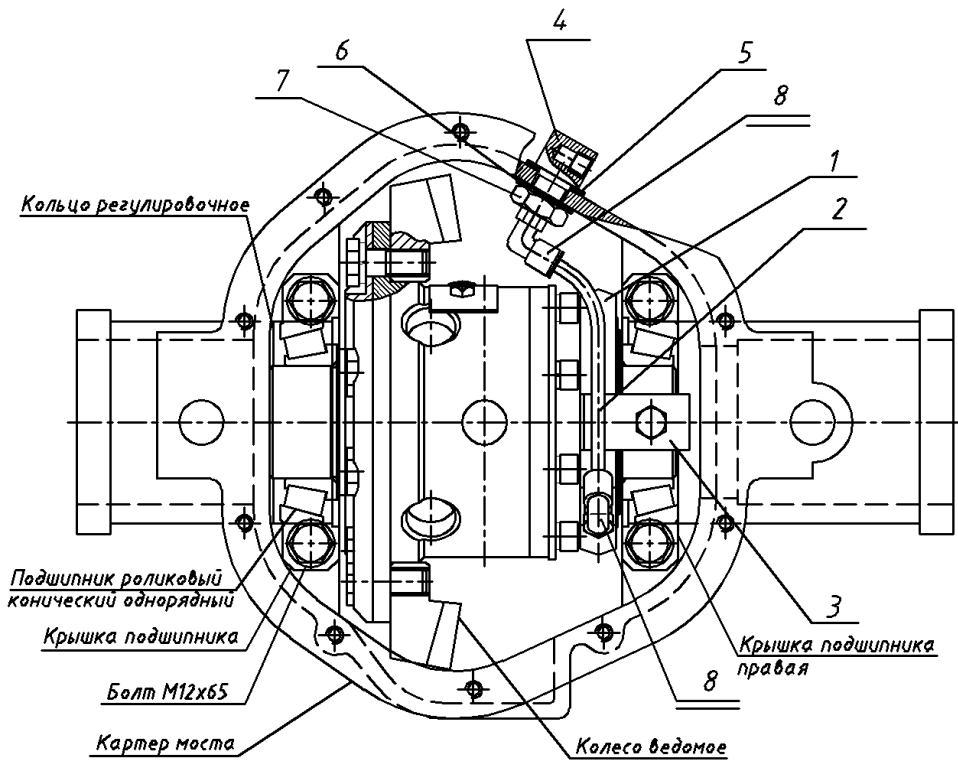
а Схема дифференциала ДБПЗ160-2403000-01 с резиновой воздухоподводящей манжетой.
